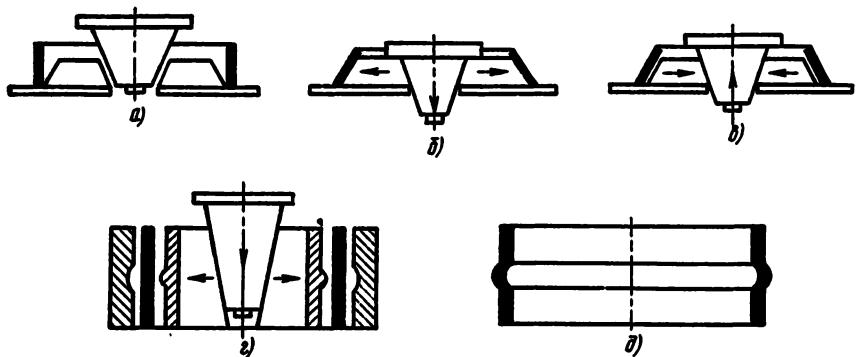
Схемы формообразования радиальным растяжением конусной заготовки:
